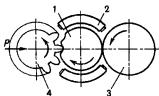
Схема горячей накатки зубьев зубчатого колеса 1-заготовка; 2 – индуктор; 3 – ролик; 4 – зубчатый валок
